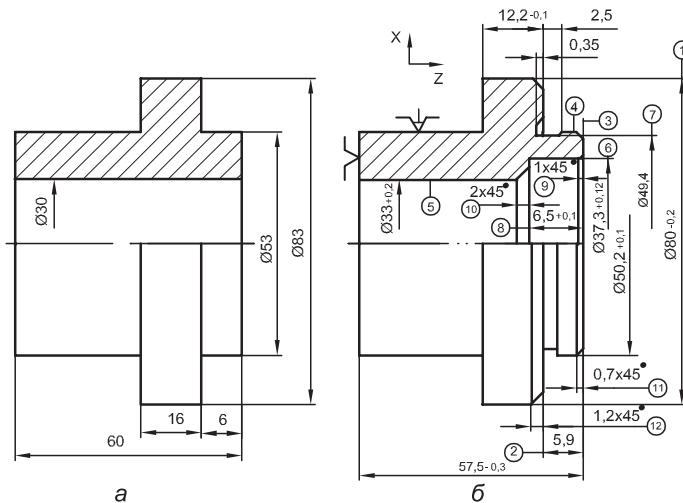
Східчаста втулка: *a* — ескіз заготовки після чорної токарної обробки; *б* — ескіз деталі після чистої токарної обробки
